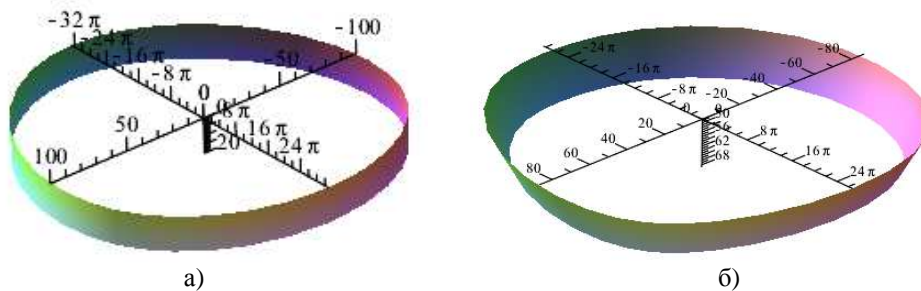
Моделирование поверхности охватывающей фрезы с радиальной конструктивной подачей при кинематической связи $t_f = -t_v$: а - соосное расположение фрезы относительно вала; б - расположение вала под углом наклона $\beta = \frac{1}{6} \pi$
